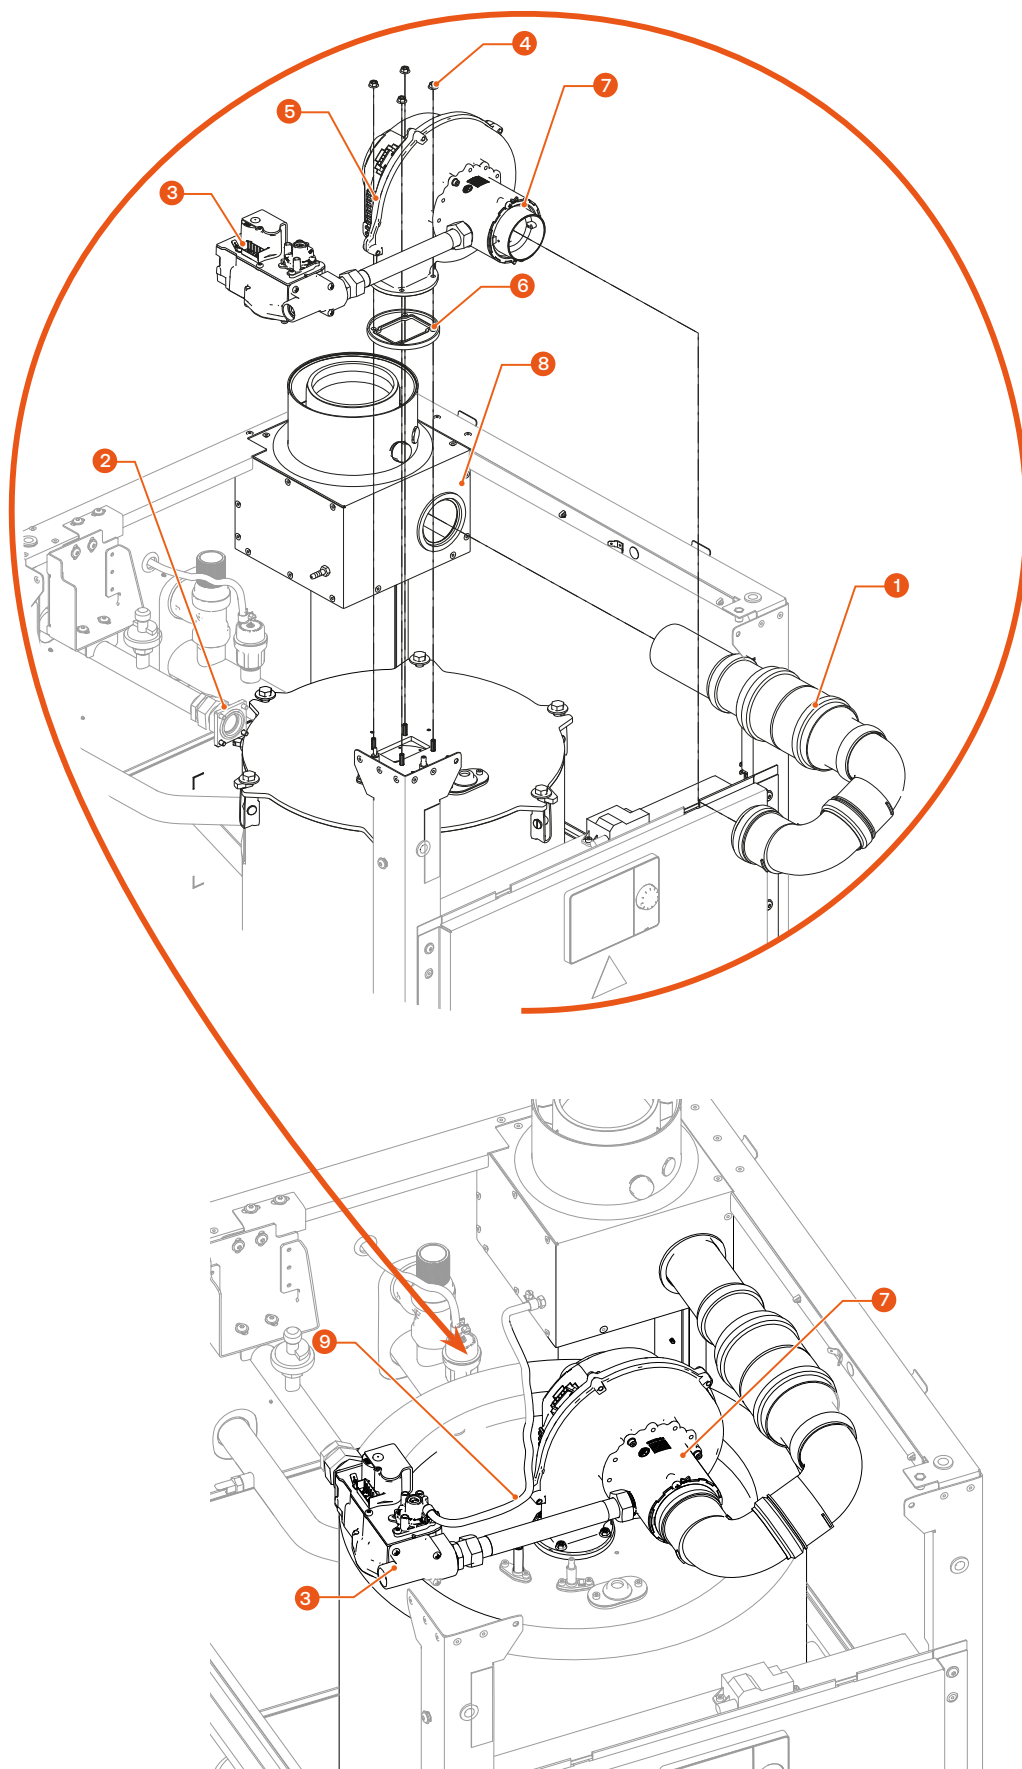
Extracción e instalación del conjunto del ventilador y el mezclador de aire-gas
